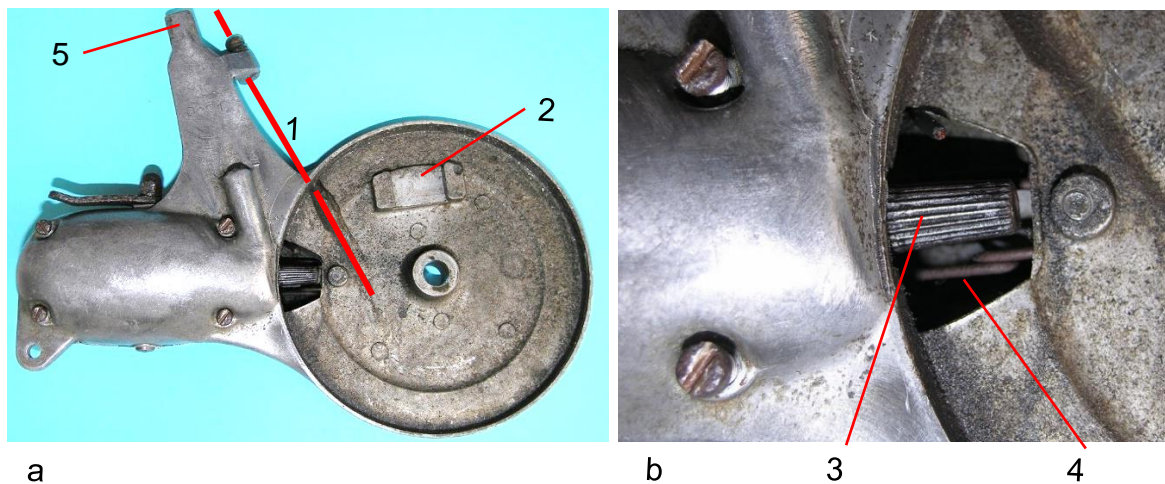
Flansch mit Generator, b) Fenster im Flansch für das Reibrad:
